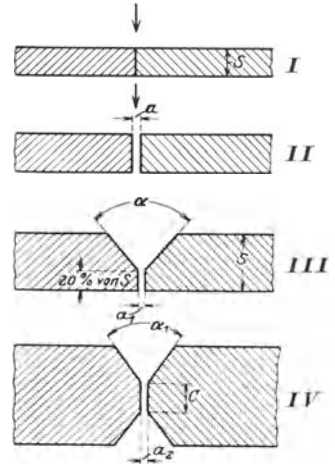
Vorbereitung von Blechen zur Stumpfschweißung.
